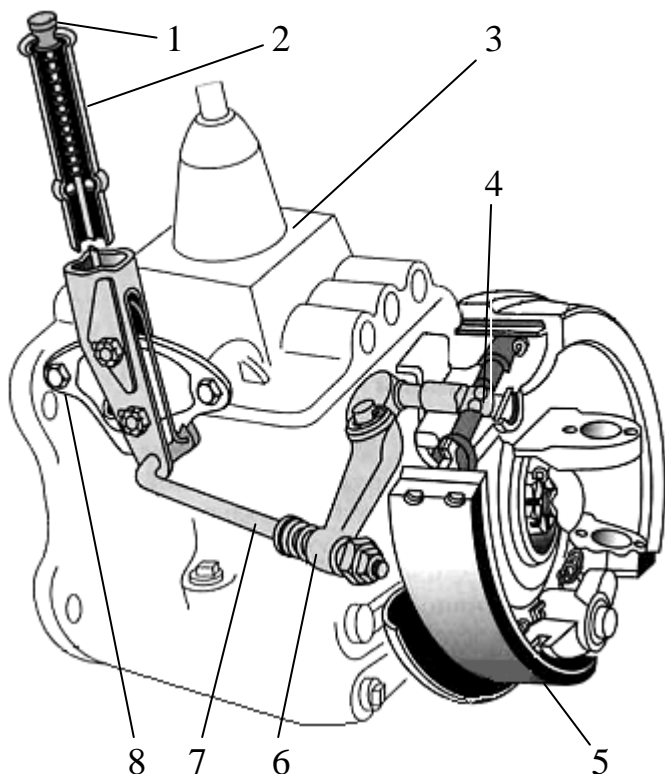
Механический привод трансмиссионного стояночного тормоза грузового автомобиля ГАЗ: 1 – кнопка фиксатора; 2 – рычаг управления стояночным тормозом; 3 – коробка передач; 4 – клиновой разжимной механизм; 5 – барабанный тормозной механизм; 6 – рычаг привода толкателя; 7 – продольная тяга; 8 – зубчатый сегмент
